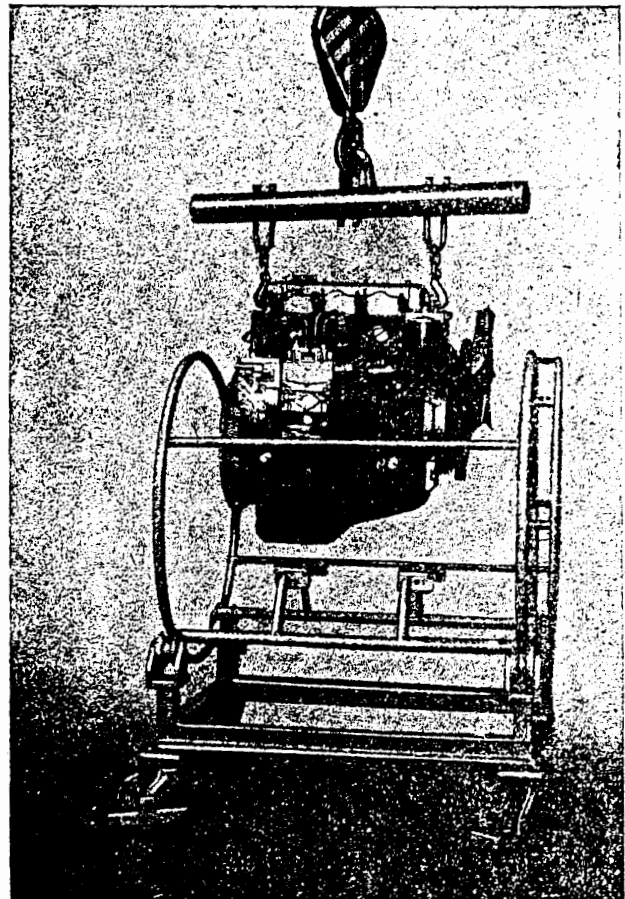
Motor mit Hebezeug auf den Montagewagen setzen
